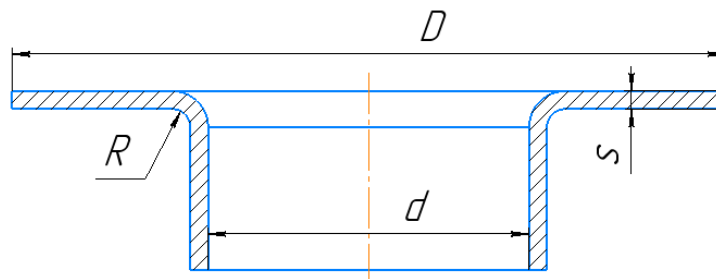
Приклад заготовки деталі типу «Фланець»
